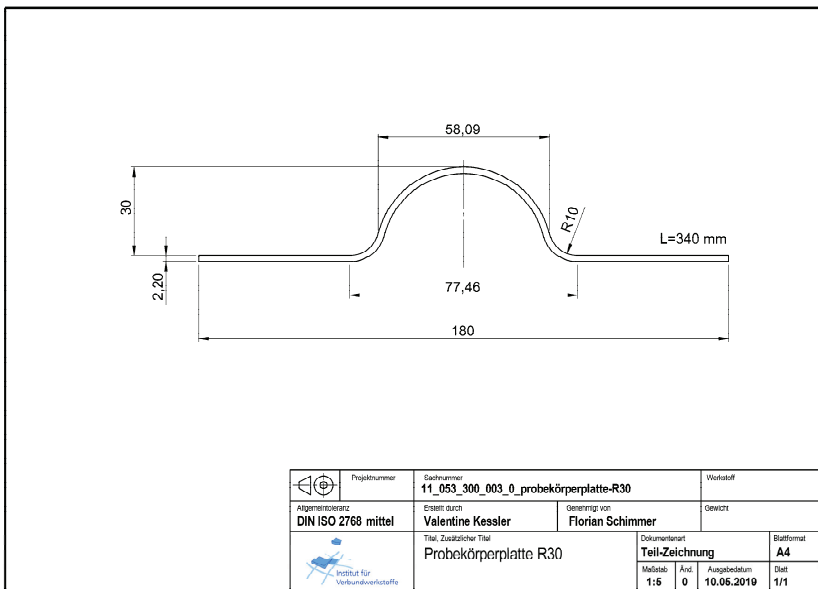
Technische Zeichnung der Ellipse R30 vor PK-Zuschnitt.
